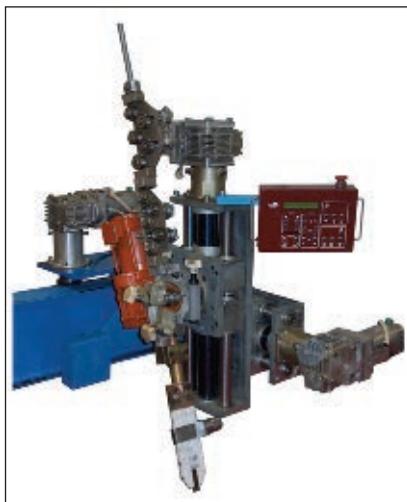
Установка КТС 4-1 для наплавки плоских поверхностей
